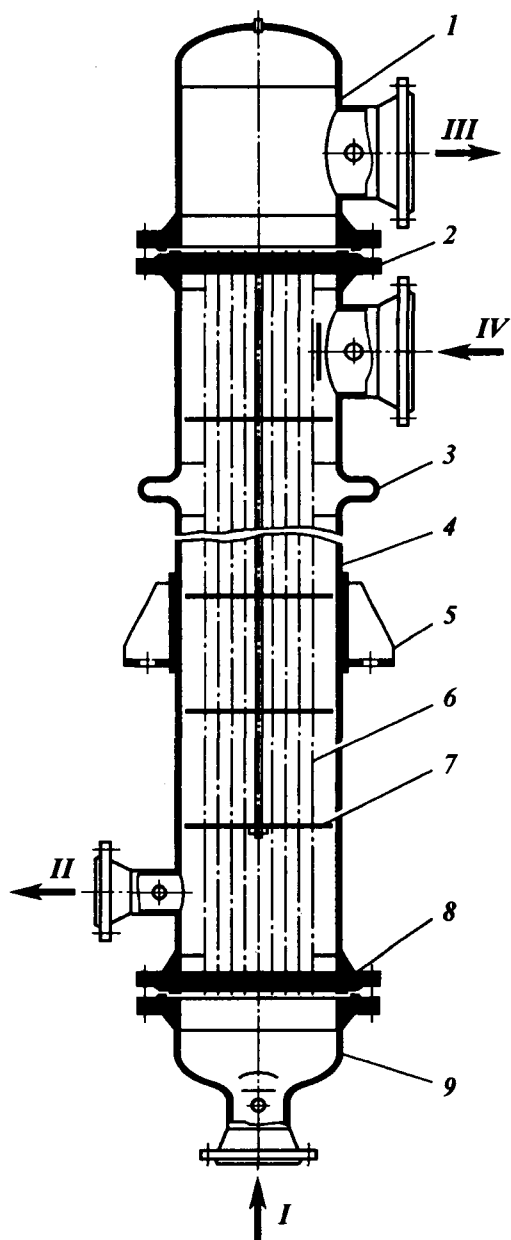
Вертикальный кожухотрубчатый испаритель с неподвижными трубными решетками и температурным компенсатором на корпусе:
